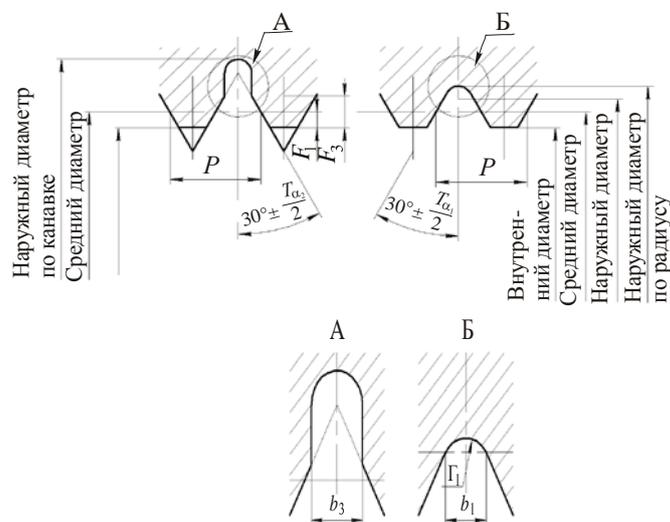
Укороченный профиль резьбы калибров-колец для метрической резьбы:
